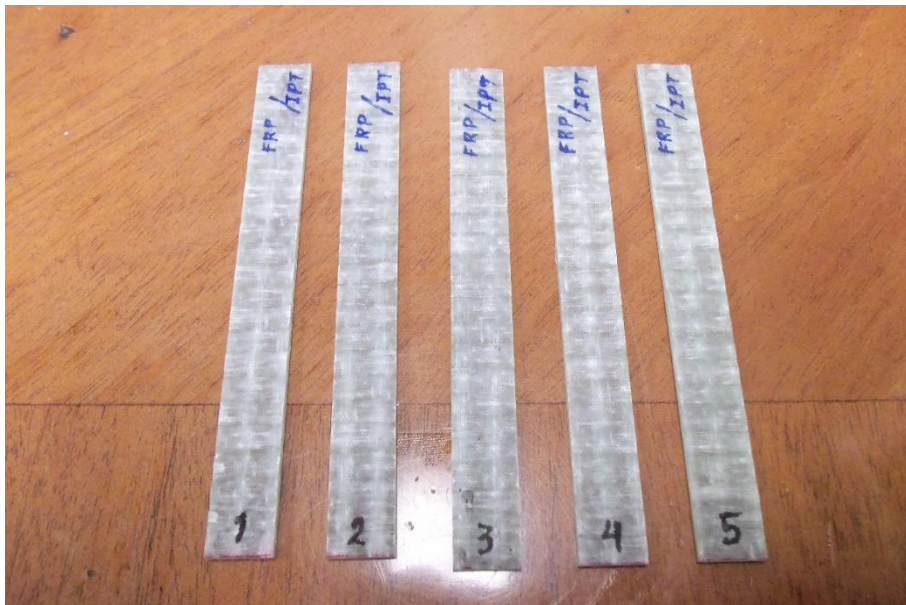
Probetas de flexión manufacturadas por infusión-presión-temperatura.
